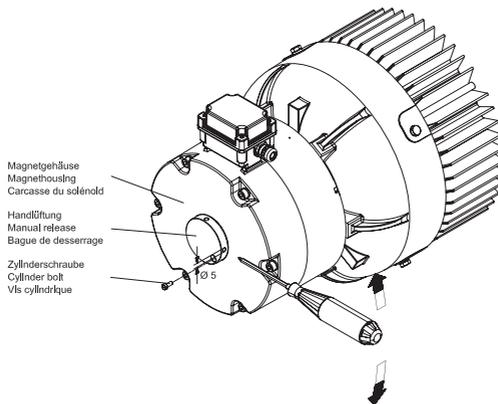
Frein de types E../Z..075 et Z..100 - avec desserrage manuel verrouillable
